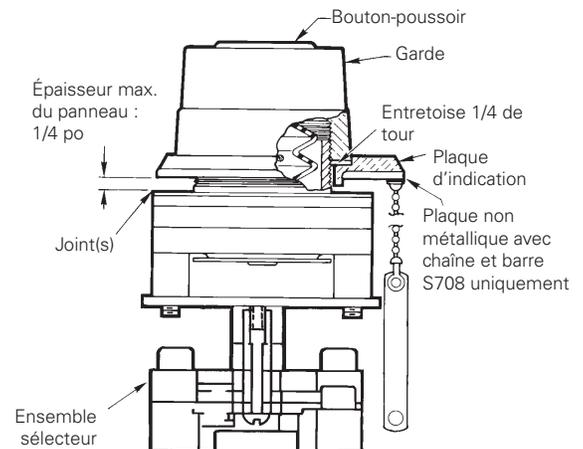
Ensemble bouton-poussoir N2PS - Vue détaillée
